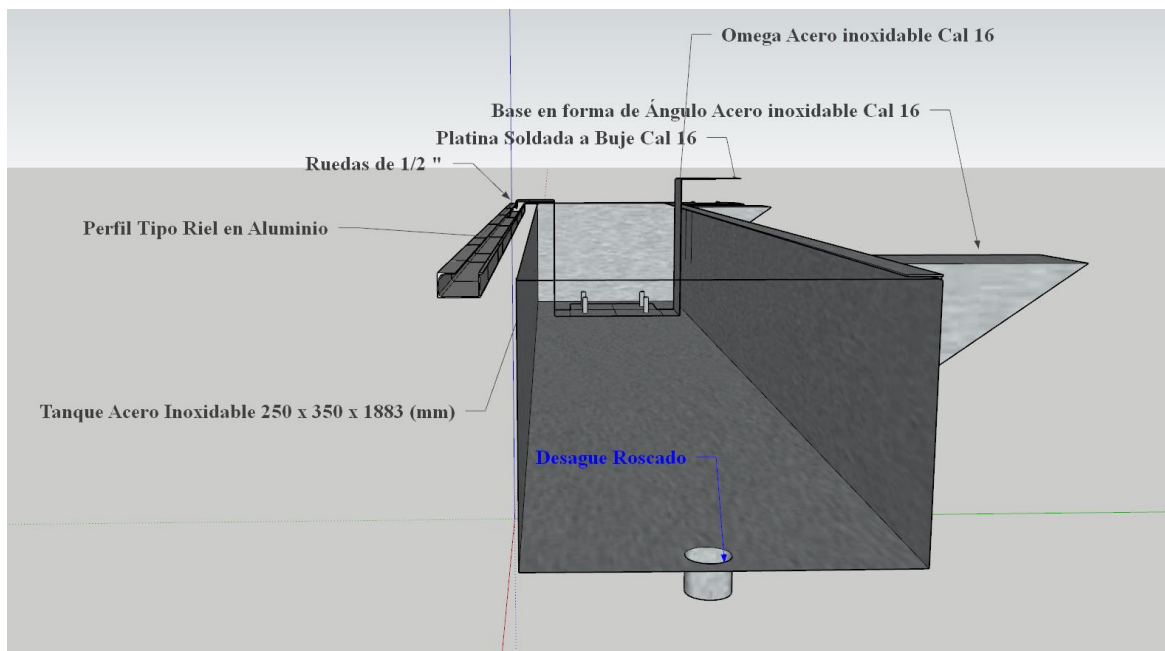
Diseño de tanque con partes soldadas, Fuente propia software utilizado (SketchUp Pro-2022)
